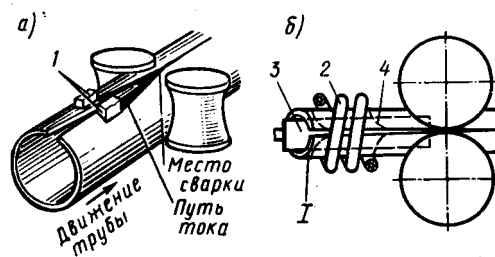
Схема контактной сварки труб токами высокой частоты:
